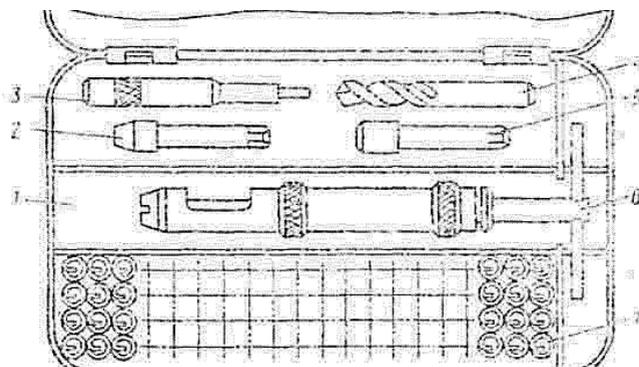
Комплект приспособлений для ремонта резьбовых отверстий спиральными вставками:
